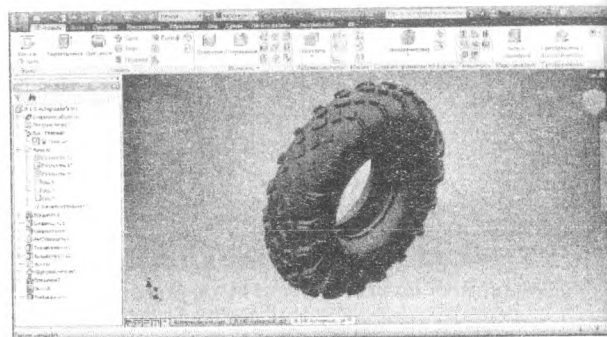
Загальний вид шини в середовищі для 3D моделювання «AUTODESK Inventor»
